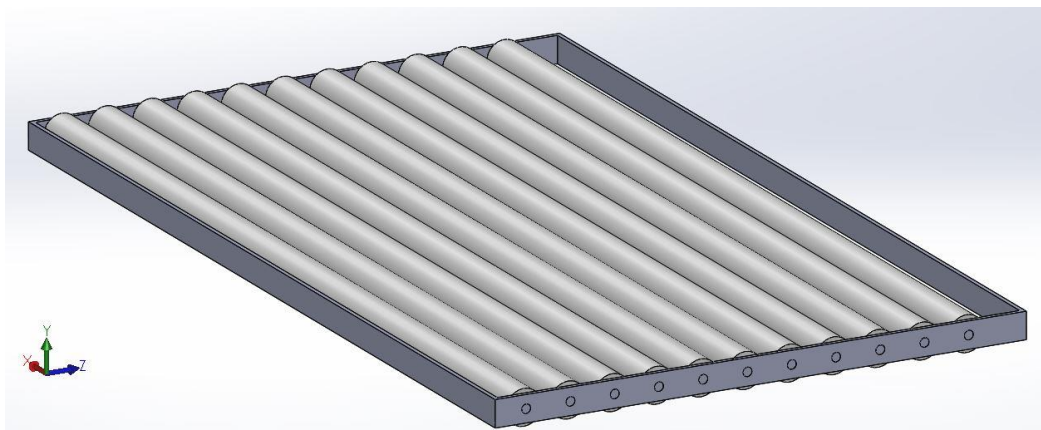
Ferdig sammenstilt løfteanretning oppheist
